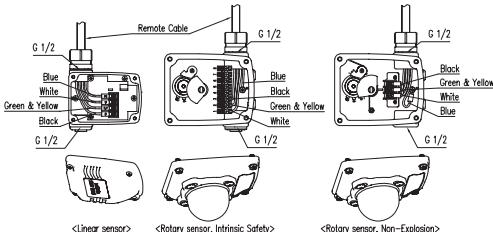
Sensore remoto e cavi di YT-2501L
